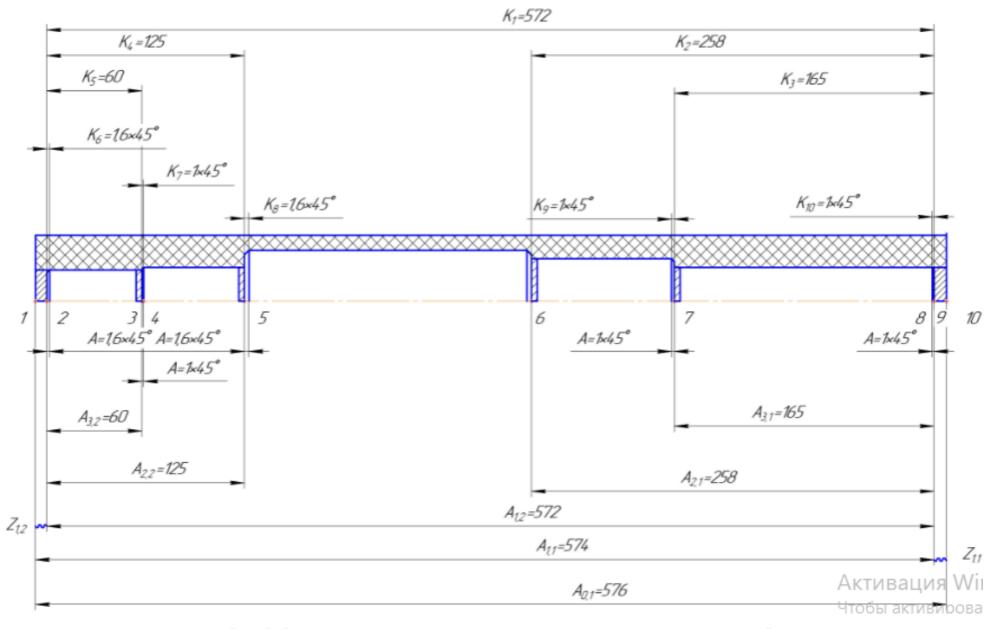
Размерная схема технологического процесса изготовления «Вал»
